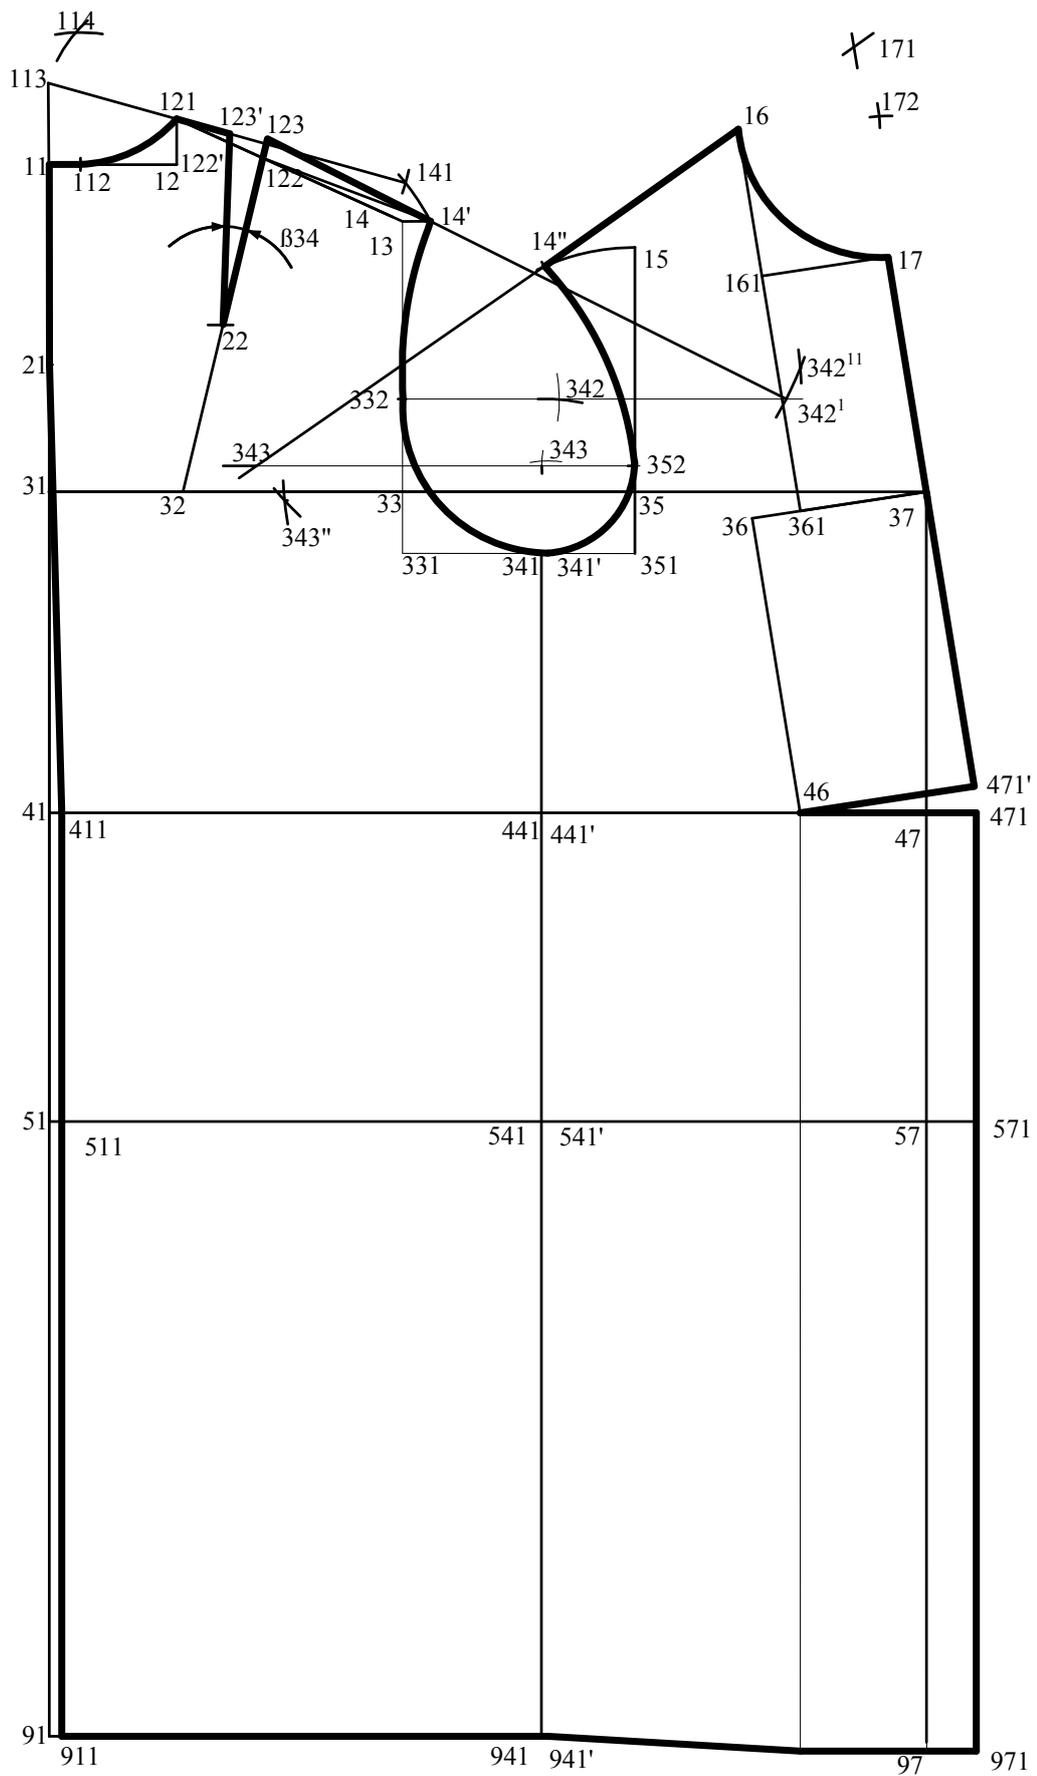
Чертеж базовой конструкции детского платья (110-56-51)
